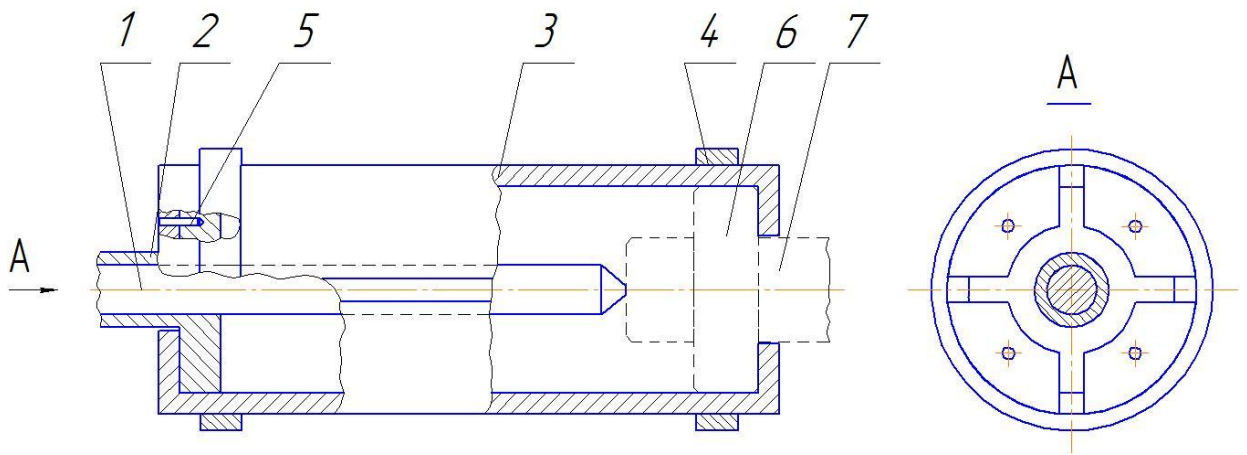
Знімач циліндричних деталей з максимальним контактом робочої поверхні лап з деталлю: 1 – шток гідроциліндра; 2 – опора; 3 – лапа; 4 – фіксує кільце; 5 – штифт; 6 – підшипник; 7 – вал.
